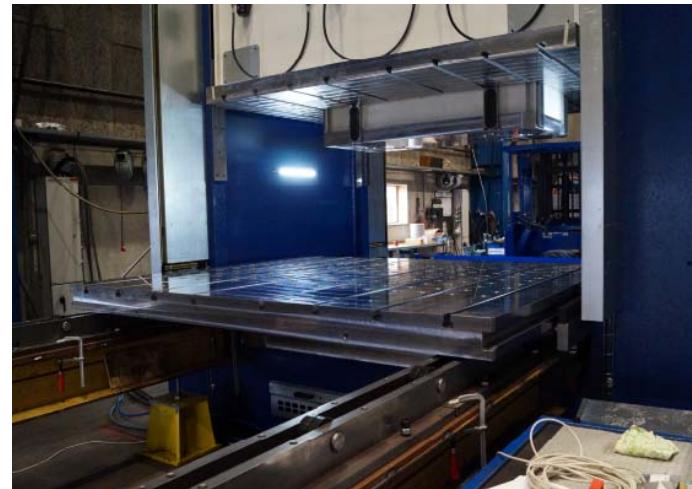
Hydraulische Dreizeige-Tiefziehpresse vom Typ TAP 1400 für einen Schweizer Premium-Hersteller für Sanitärwannen.
